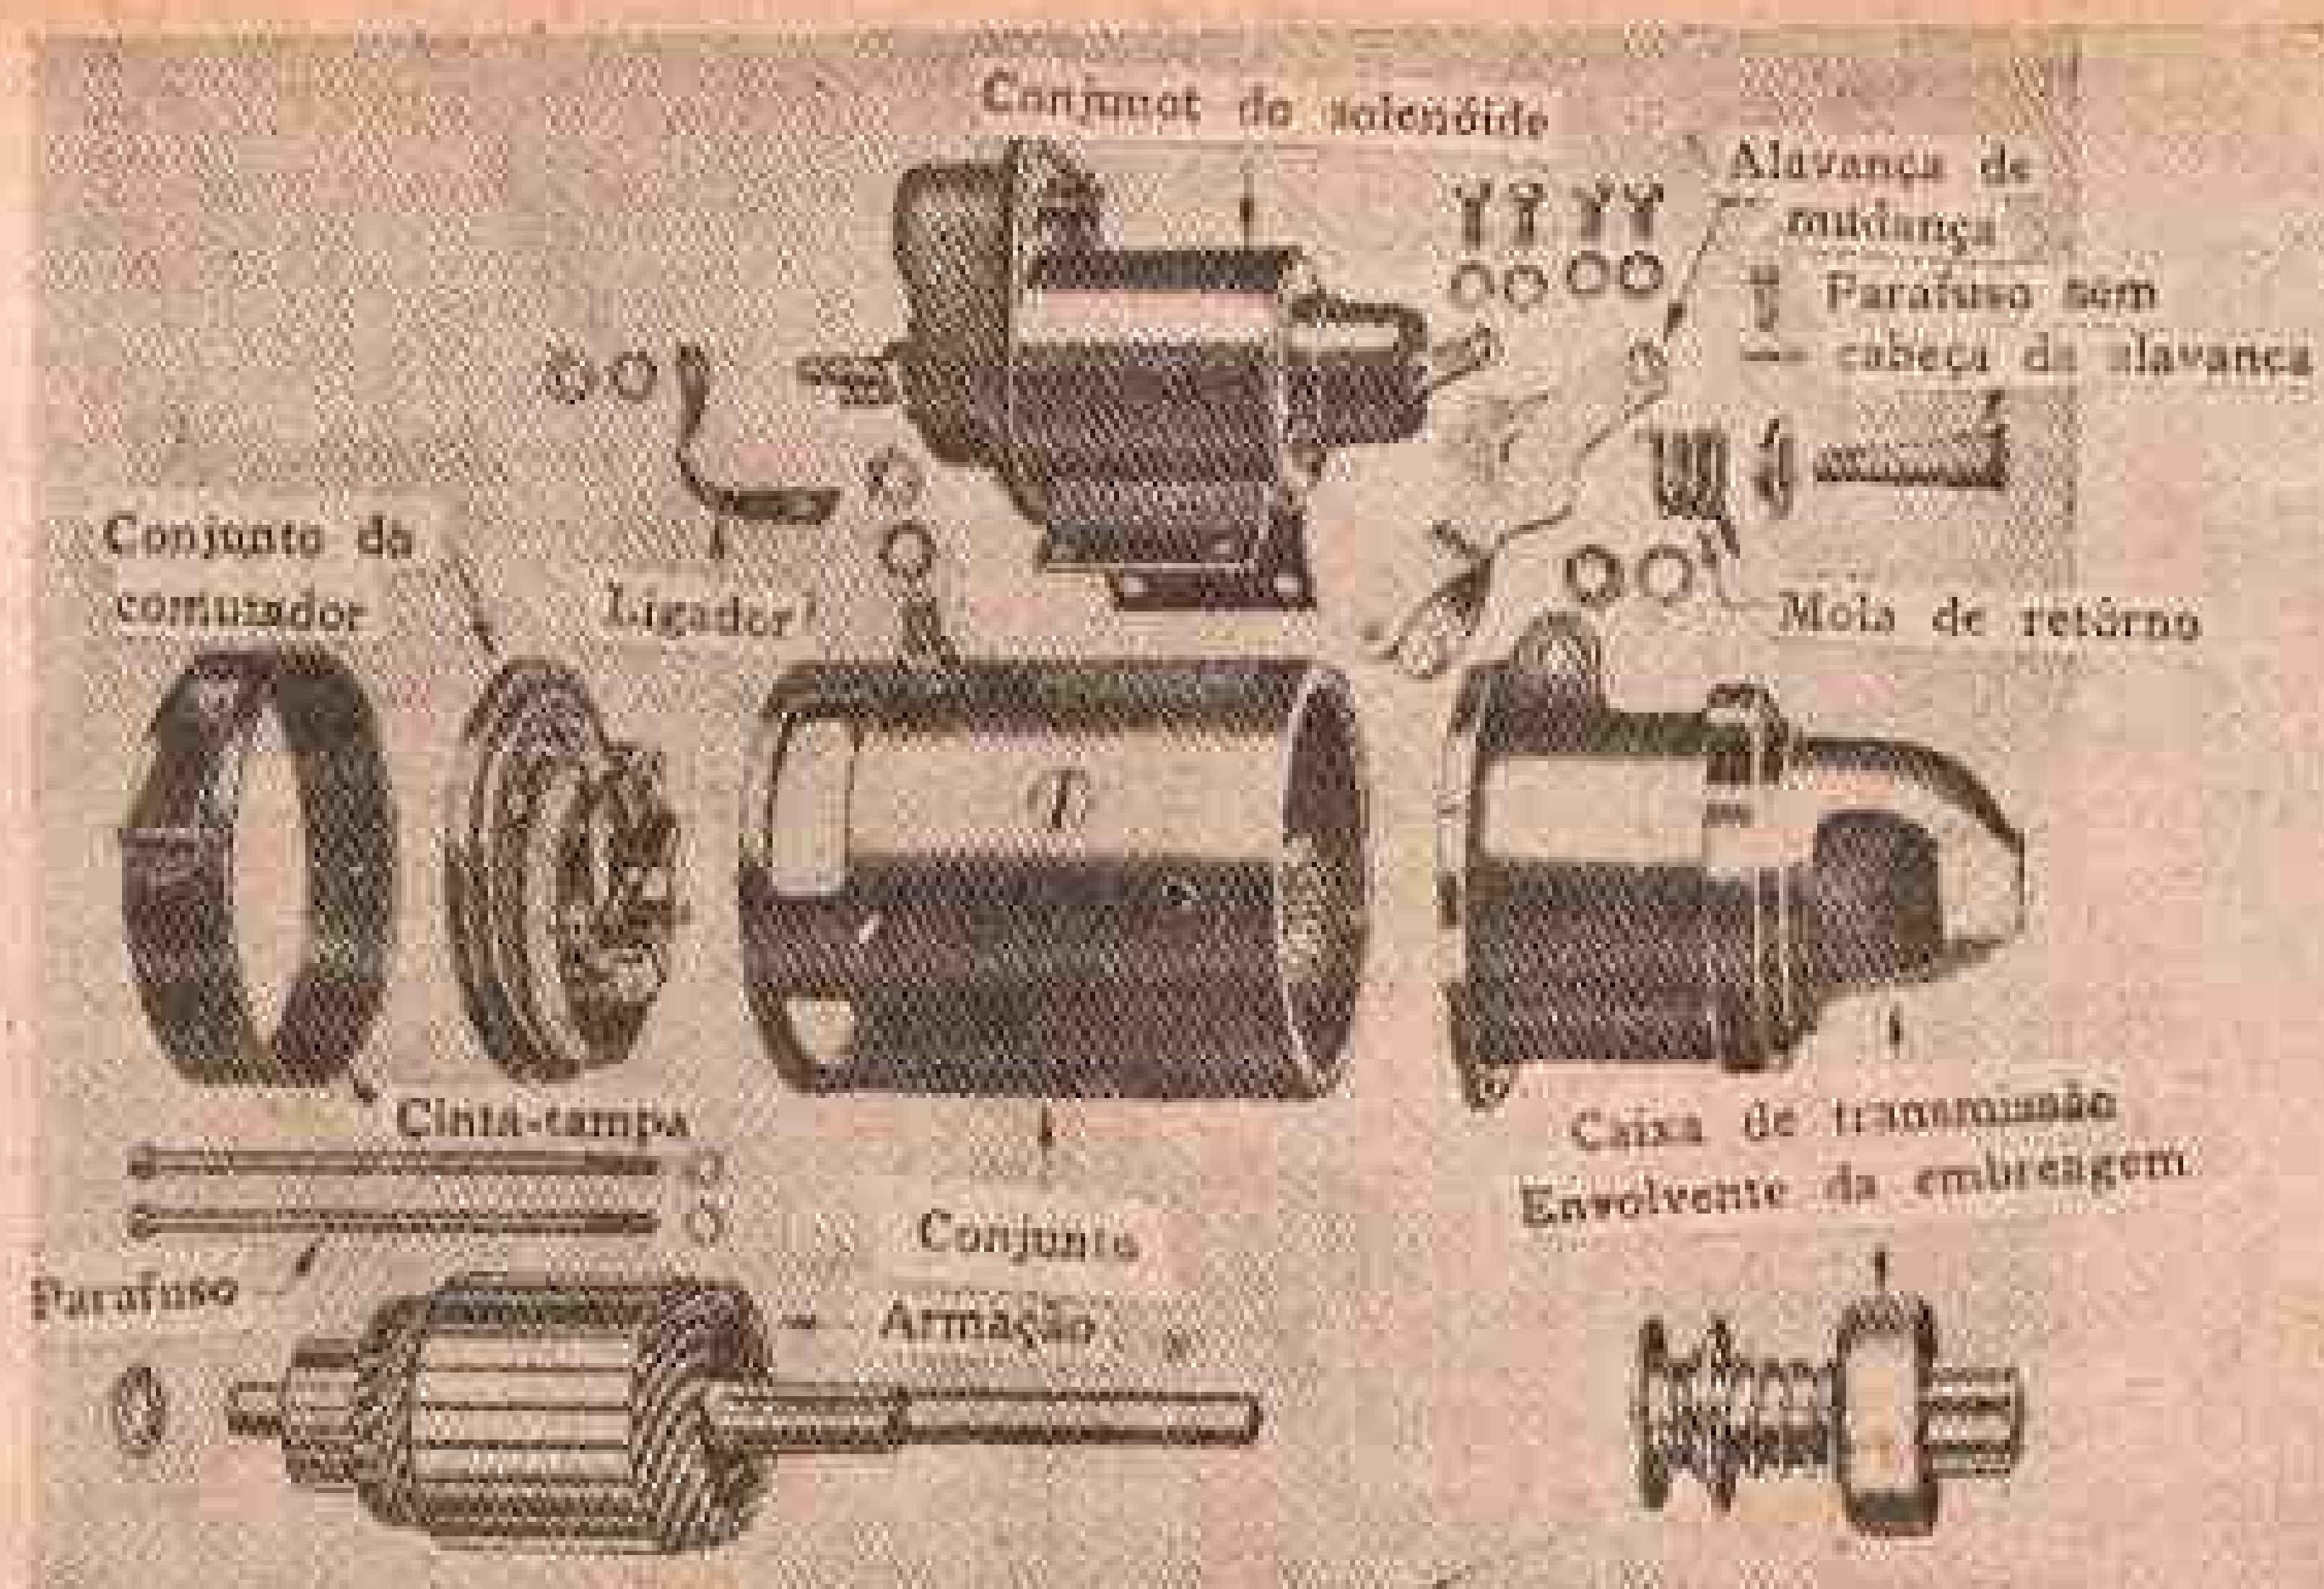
Motor de arranco de carro de passageiros, desmontado.
